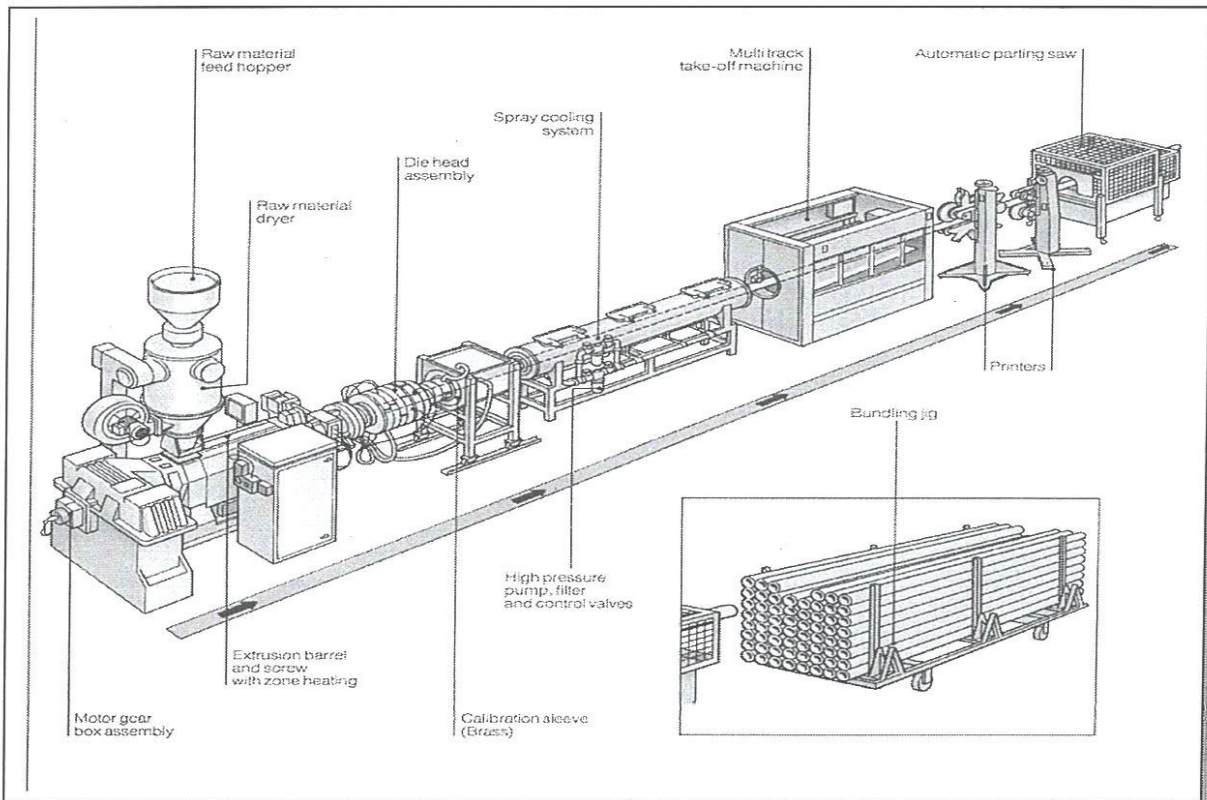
Vue d'ensemble d'une extrudeuse.
